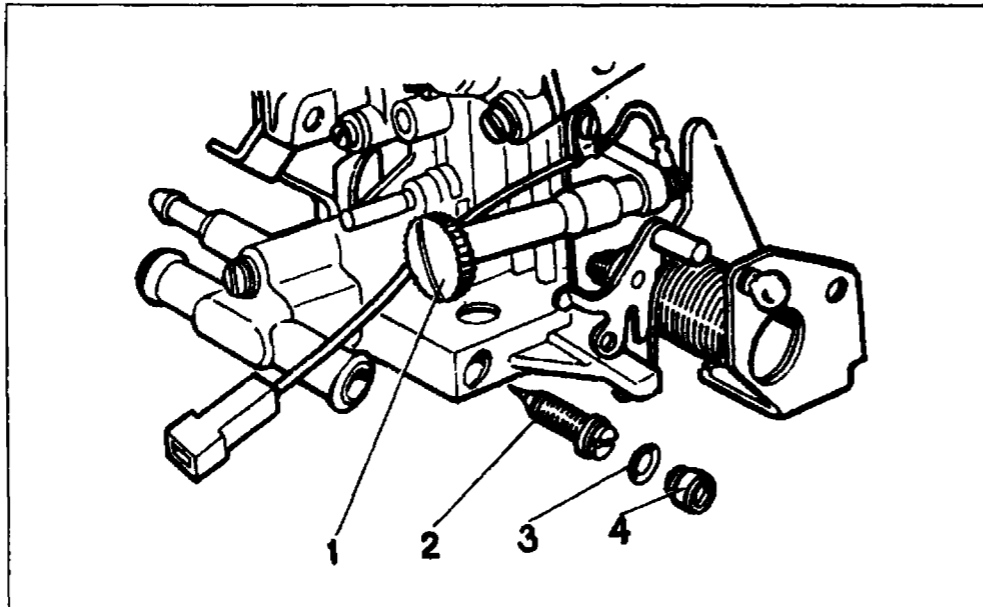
Винты регулировки системы холостого хода карбюратора: 1 — регулировочный винт количества смеси; 2 — регулировочный винт качества (состава) смеси; 3 — уплотнительное кольцо; 4 — заглушка регулировочного винта
